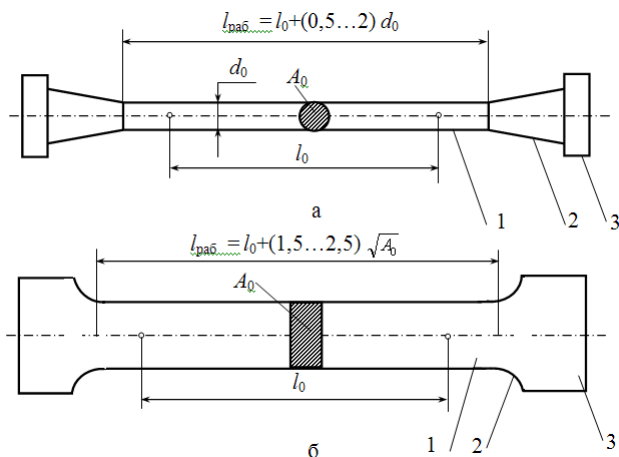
Цилиндрический (а) и плоский (б) образцы
